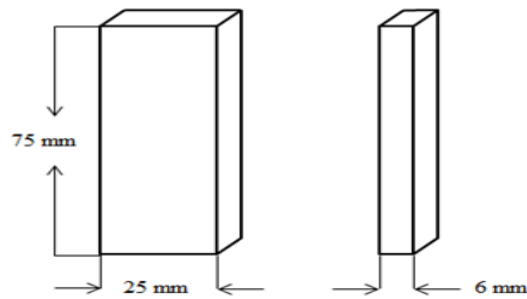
Dimensiones de la probeta de ensayo de abrasión.
